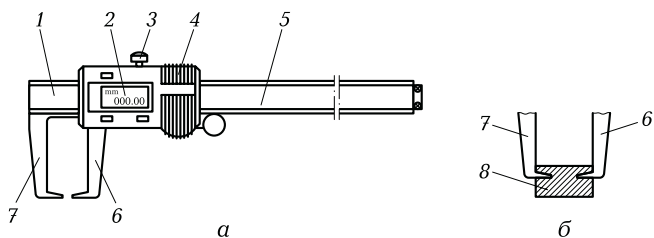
Специальный штангенциркуль с цифровой индикацией для измерения размеров между канавками на наружных поверхностях заготовки (а) и схема измерения (б):
